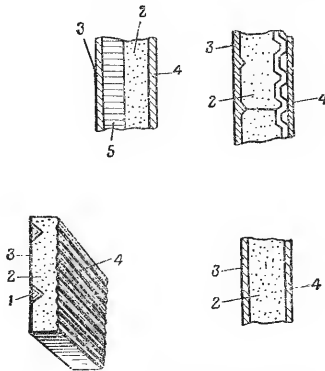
Разновидности конструкции оболочки корпуса космической станции (КС): 1 — стрингер; 2 — слой пенопласта; 3 — оболочка корпуса; 4 — буферная оболочка; 5 — сотовая конструкция с полиуретановым наполнителем
